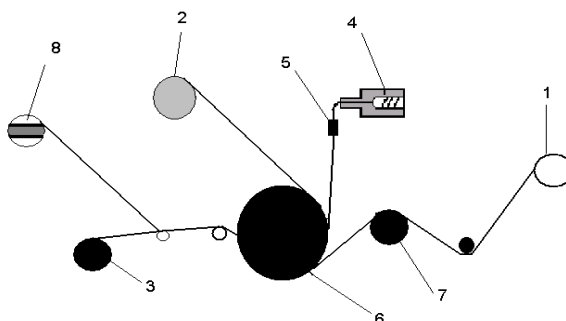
Схема адгезійного ламінування за допомогою клею-розплаву: 1 – плівка; 2 – плівка; 3 – пристрій для намотки; 4 – екструдер; 5 – плоскощільна головка; 6 – охолоджуючий барабан; 7 – прижимний валик; 8 – структура матеріалу.
